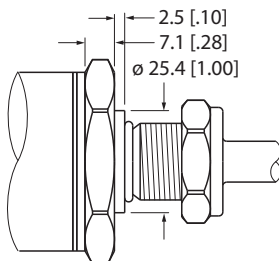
Ausführung mit Raised Face (R10)– Gehäusemutter mit Gewinde
